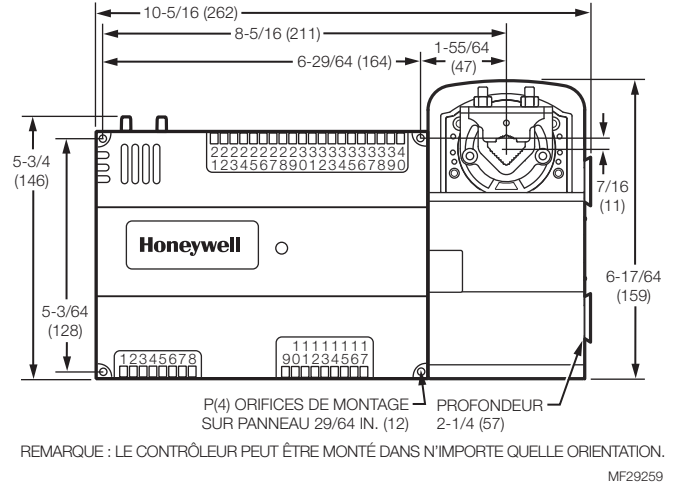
Modèle PVB6436AS à montage sur panneau, dimensions en pouces (mm).
